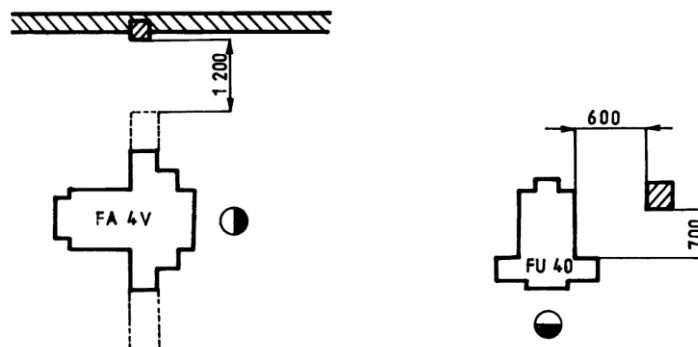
Vzdálenosti stroje a dopravních cest [8].
